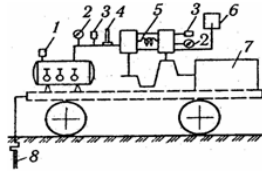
Схема пересувної компресорної установки: 1 - ресивер; 2 - манометр; 3 - запобіжний клапан; 4 - термометр; 5 - холодильник; 6 - фільтр; 7 - двигун; 8 - робоче заземлення.
